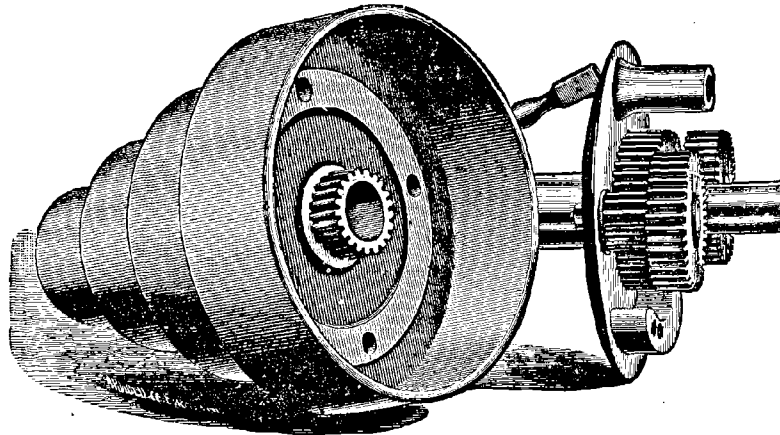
Dispositif du double harnais d'engrenages de la machine Barnes.
